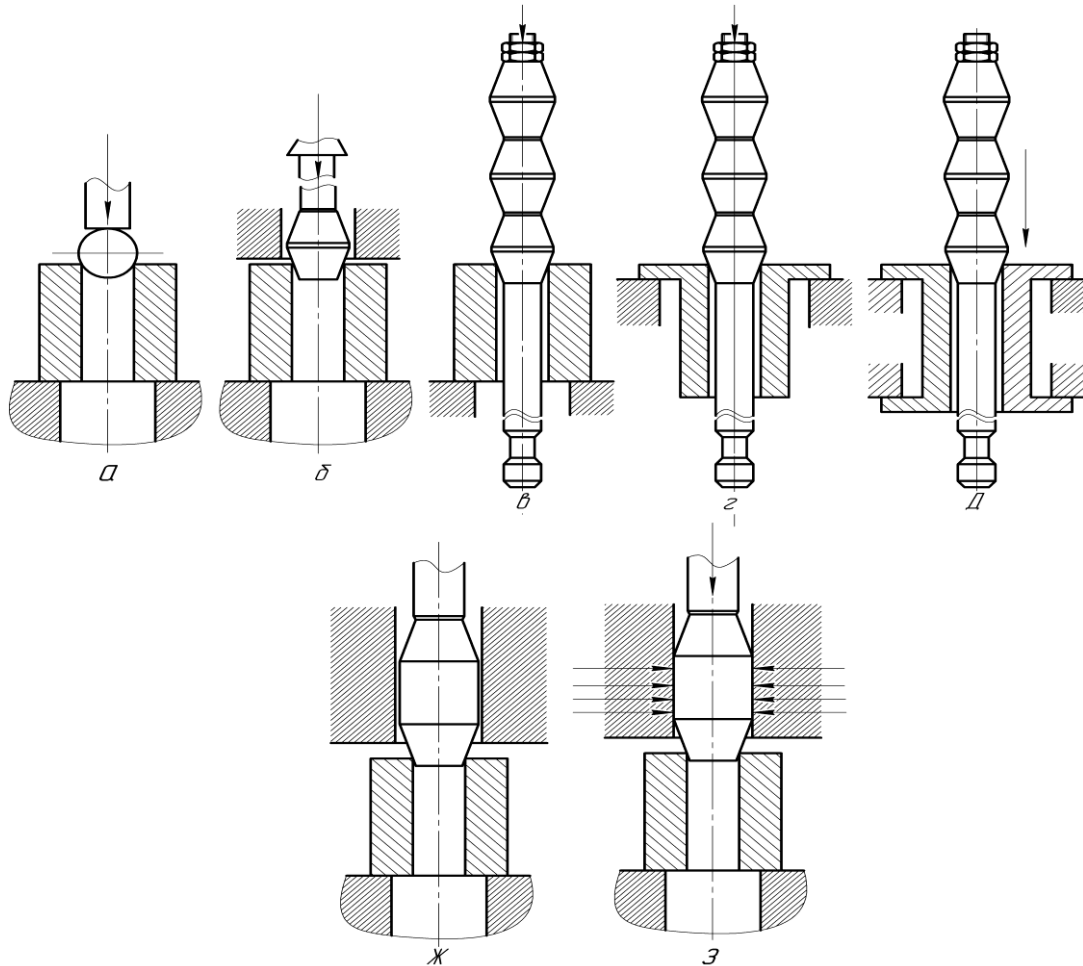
Схема дорнования отверстия : (а) шаром (со сжатием заготовки); (б) консольно закрепленной однозубой прошивкой (со сжатием заготовки); (в) многозубым дорном-протяжкой (со сжатием заготовки); (г) многозубым дорном-протяжкой (со растяжением заготовки); (д) многозубым дорном-протяжкой (со осевым заневоливанием заготовки); (е) однозубой незакрепленной в осевом направлении прошивкой, размещенной с зазором в направляющей втулке (со сжатием заготовки); (ж) однозубой незакрепленной в осевом направлении прошивкой, размещенной с натягом в направляющей втулке (со сжатием заготовки);
